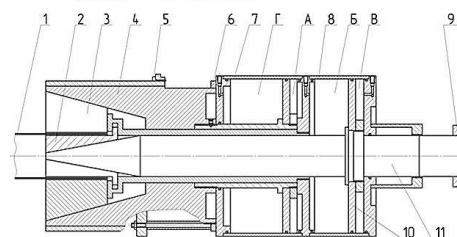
Гидравлическая калибрующая головка: 1 - деталь; 2 – пуансон; 3 – матрица; 4 – обжимная втулка; 5 – концевой выключатель; 6 - кольцо-фиксатор; 7,8 - силовые цилиндры; 9 - кольцо-фиксатор; 10 – поршень цилиндра привода пуансона; 11 - шток цилиндра привода пуансона; А - поршневая полость привода матрицы; Б - штоковая полость привода пуансона; В - поршневая полость привода пуансона; Г - штоковая полость привода матрицы
